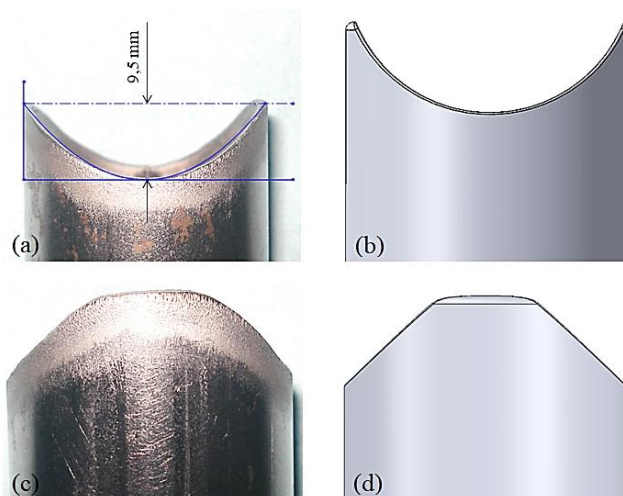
Configuração geométrica no posicionamento para soldagem.
